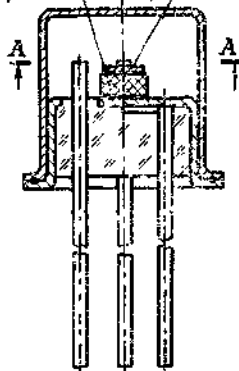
Конструкция корпуса КТ-21. Вариант для монтажа кристалла на вывод корпуса.
